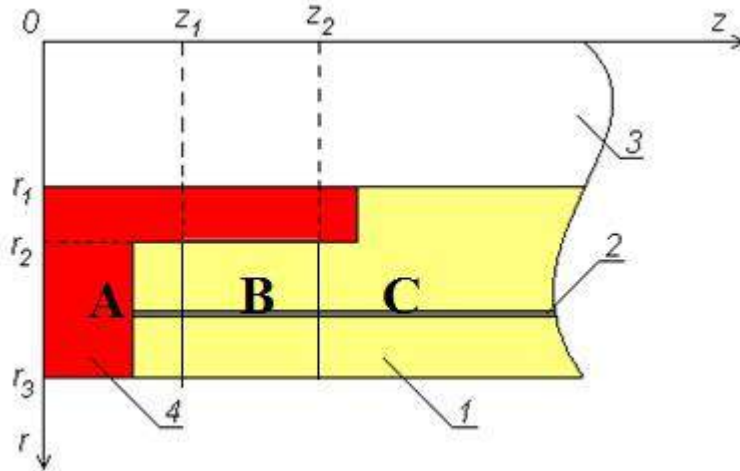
Расчетная схема трубы с гильзой: 1 – стенка трубы; 2 – армирующий слой; 3 – воздух внутри трубы; 4 – сварочная гильза, зона А, В, С.
